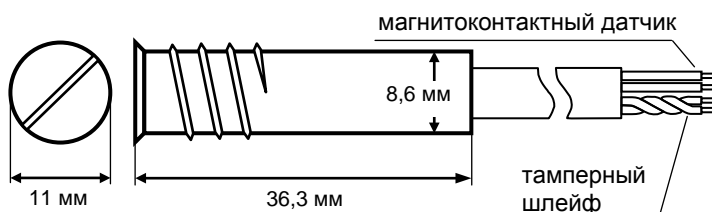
Геркон извещателя S-3 в металлическом корпусе
